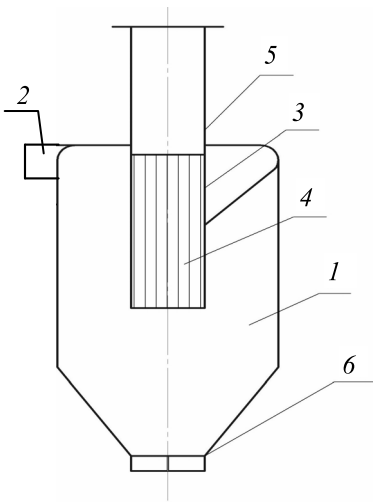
Пилувловлювач: 1 – циліндрично-конічний корпус пилувловлювача; 2 – тангенційний вхідний патрубок; 3 – жалюзійний відокремлювач; 4 – жалюзі; 5 – вихлопний патрубок; 6 – пиловипускний патрубок.
